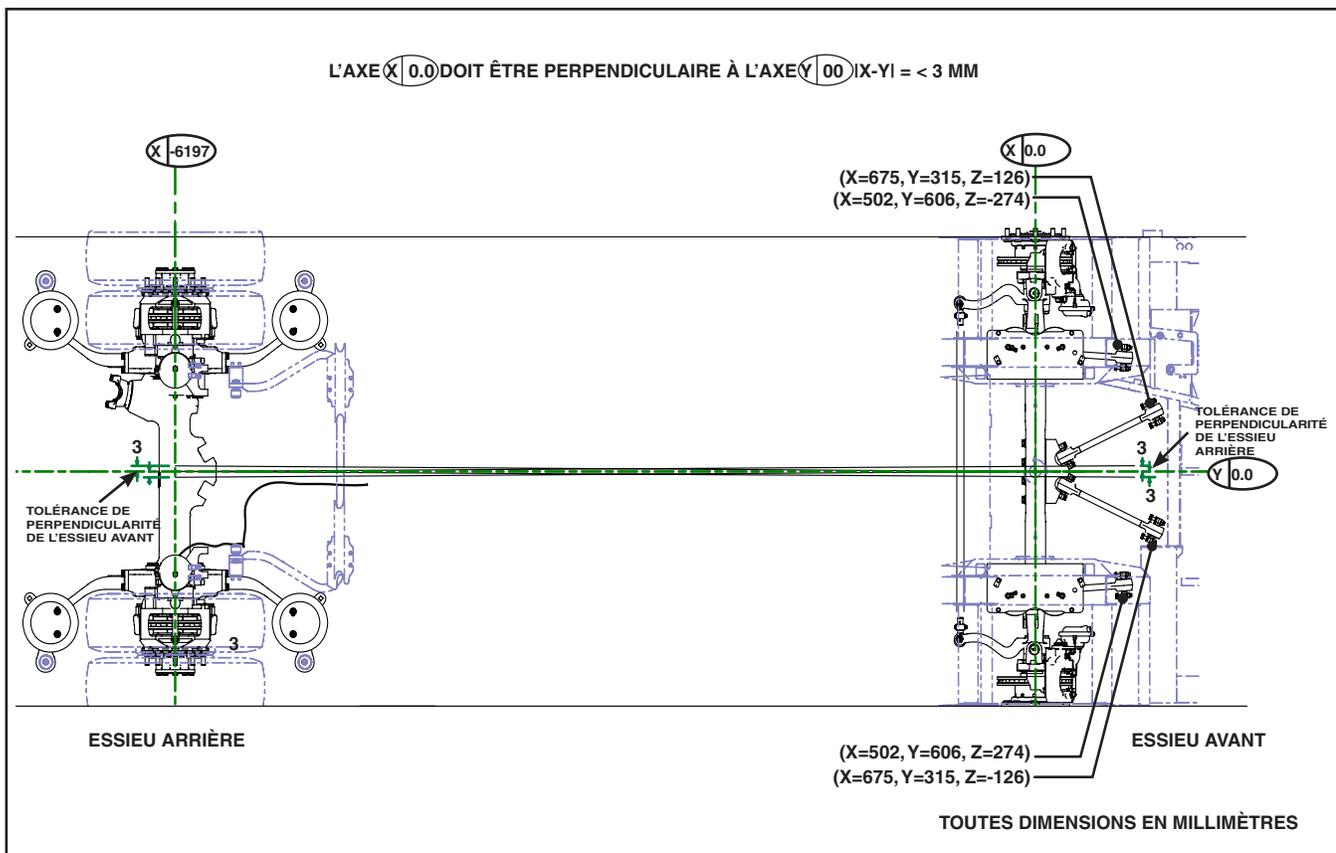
Alignement de l'essieu arrière et de l'essieu avant
